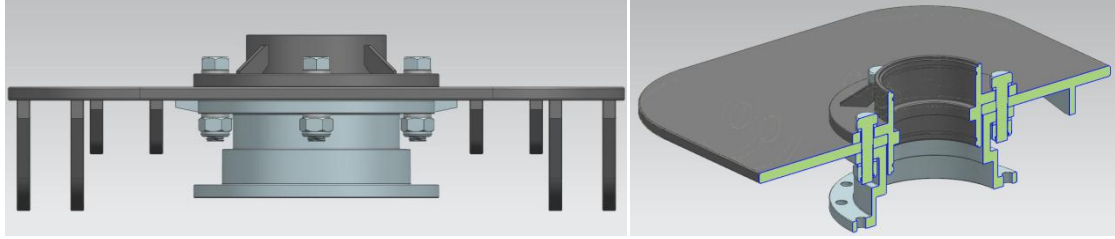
33. Disseny del conjunt de la brida, la taula i el suport motor, amb la unió cargolada.
